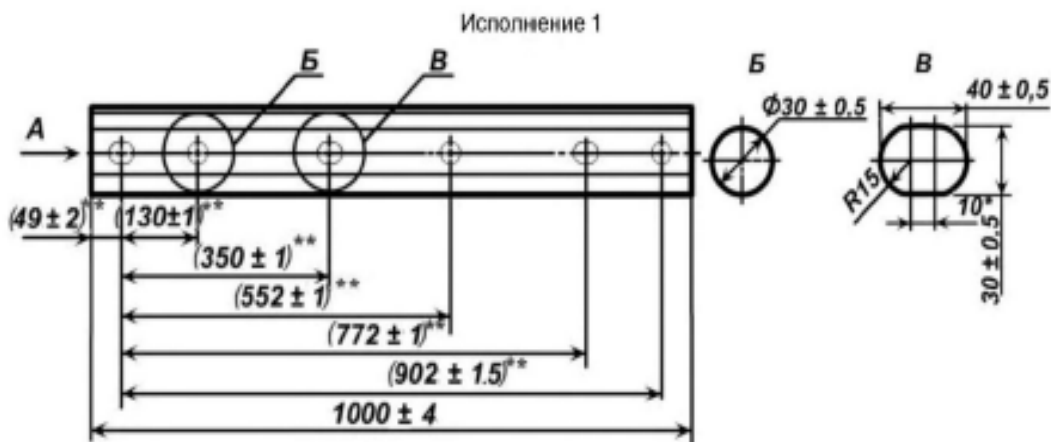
Конструкция и размеры накладок для рельсов типа Р65
